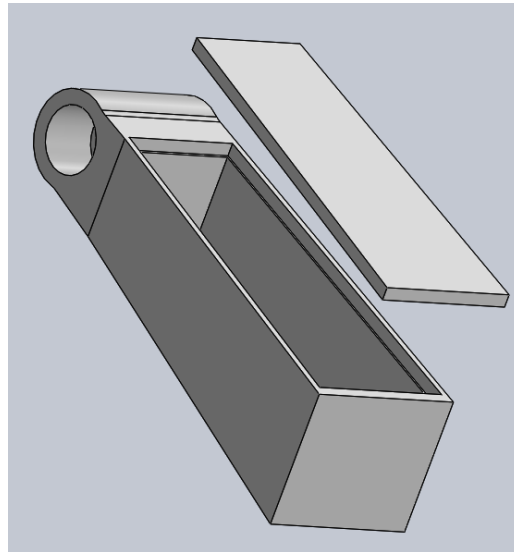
Vista explosionada del subensamblaje lateral izquierdo. [2]
